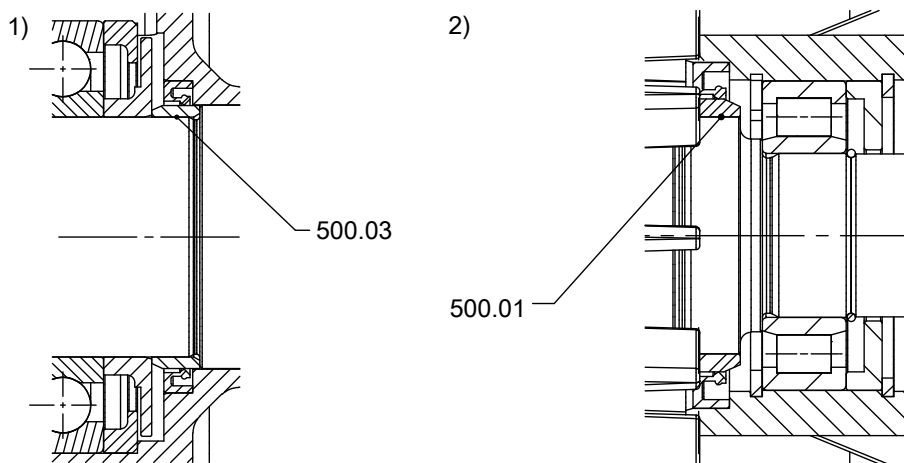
Подшипниковые опоры — насосный агрегат без системы охлаждения
